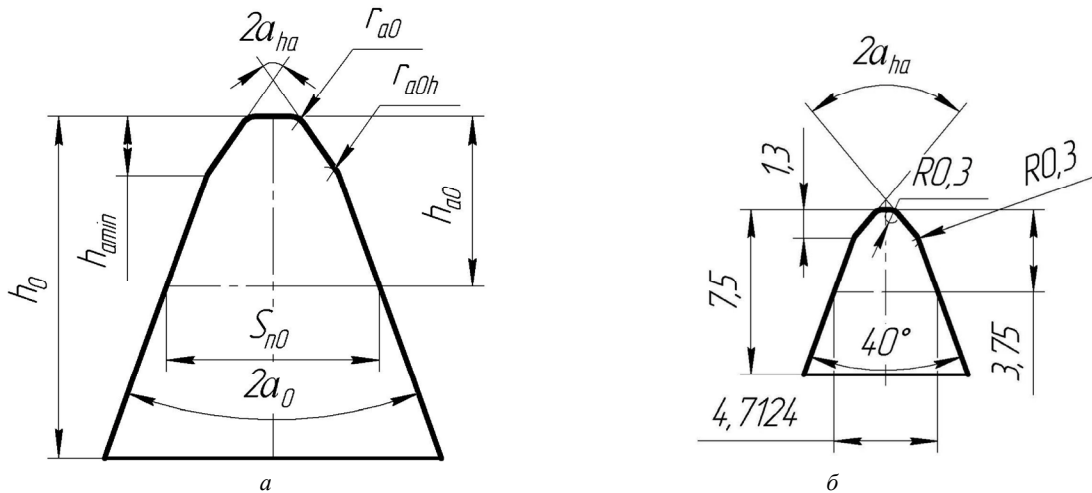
а) профіль зуба фрези, що дозволяє виключити особливу точку на поверхні зубчастого колеса, що обробляється. б) розрахунковий профіль ВІП конвольютної черв'ячної фрези призначеної для формування без підрізання зубчастого колеса:  $m=3$ ,  $Zk=10$ ,  $x=+0.3485$ ,  $\beta_0=0^0$ , діаметр вершин зубів колеса  $d_{a1}=38.1$ , діаметр западин  $d_{f1}=24.7$ , фреза конвольютна  $d_a=80$ ,  $r_{a0}=0.05$
